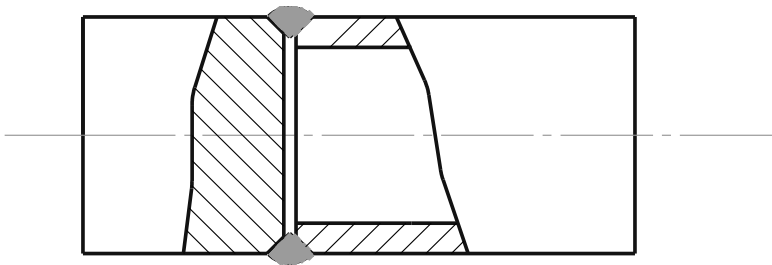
Сварка трубы со стержнем встык с предварительной разделкой кромок
